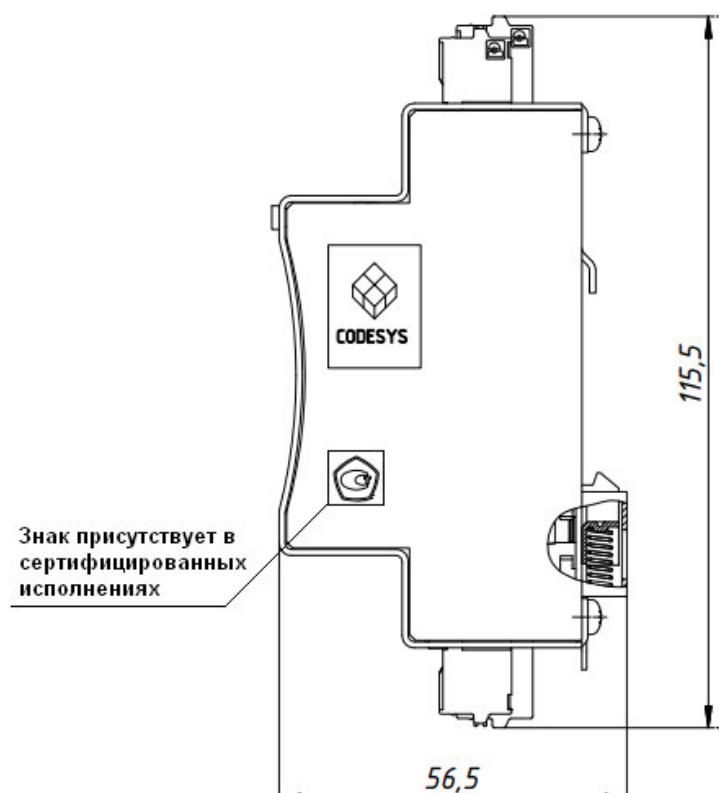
Контроллер. Габаритно-установочный чертеж. Вид сбоку
